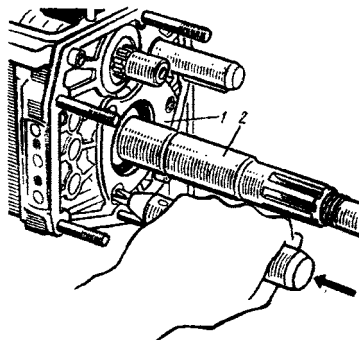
Снятие стопорной пластины промежуточного подшипника вторичного вала коробки передач
